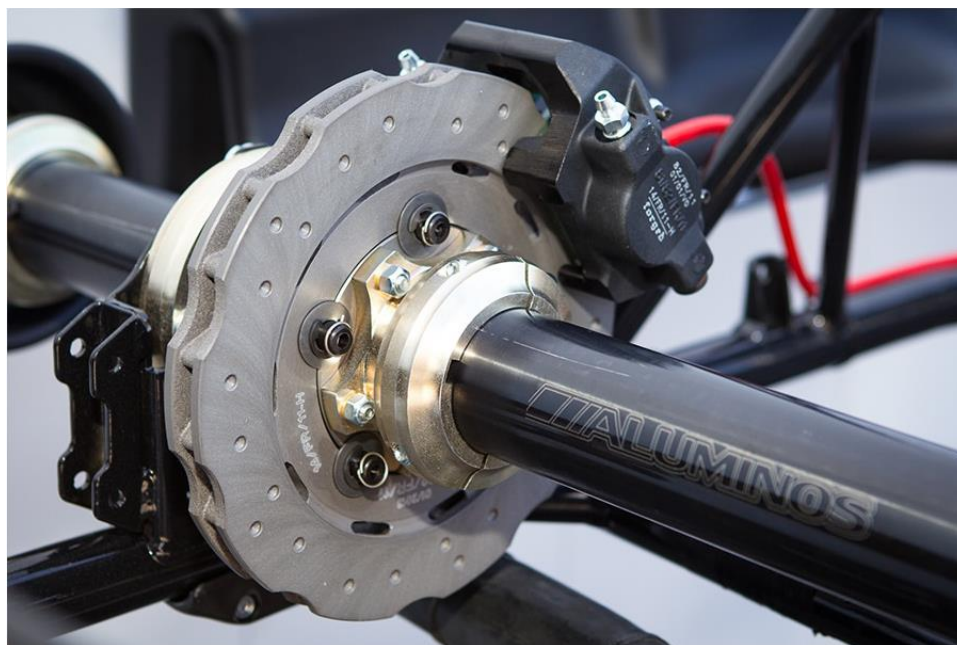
detalle de montaje del disco de freno. Fuente: <http://www.cameronkarting.com>
